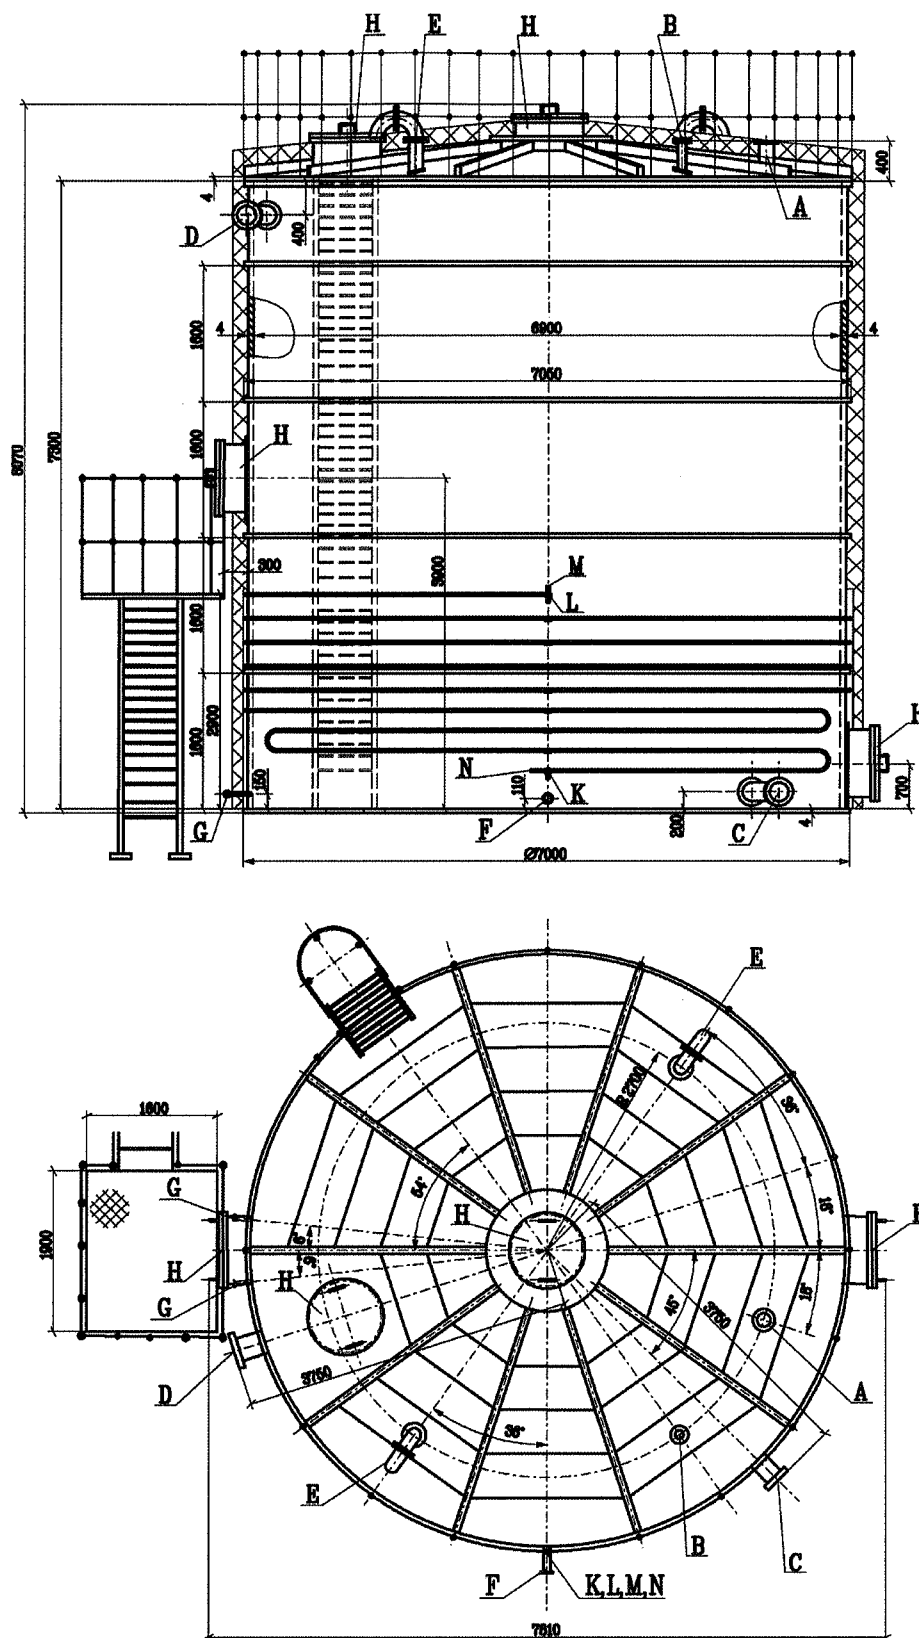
Габаритный чертеж бака собственных нужд ВПУ
